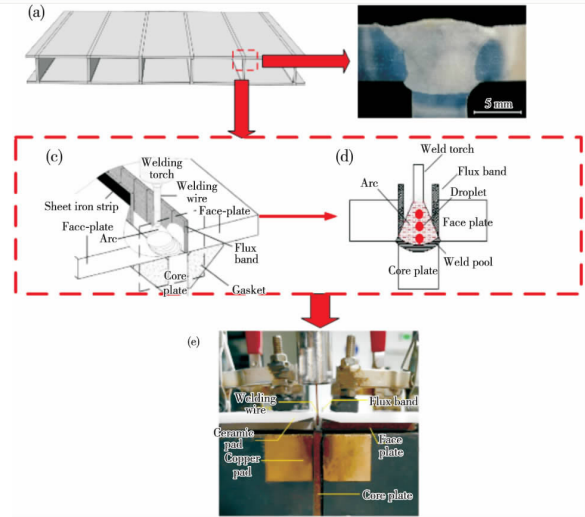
约束良好情形下 FBCA 所得三明治板接头: (a) I 型三明治板结构; (b) FBCA 焊接 T 形接头焊缝; (c) FBCA 焊接示意图; (d) 焊接时焊剂片约束示意图; (e) T 形接头装配方式
